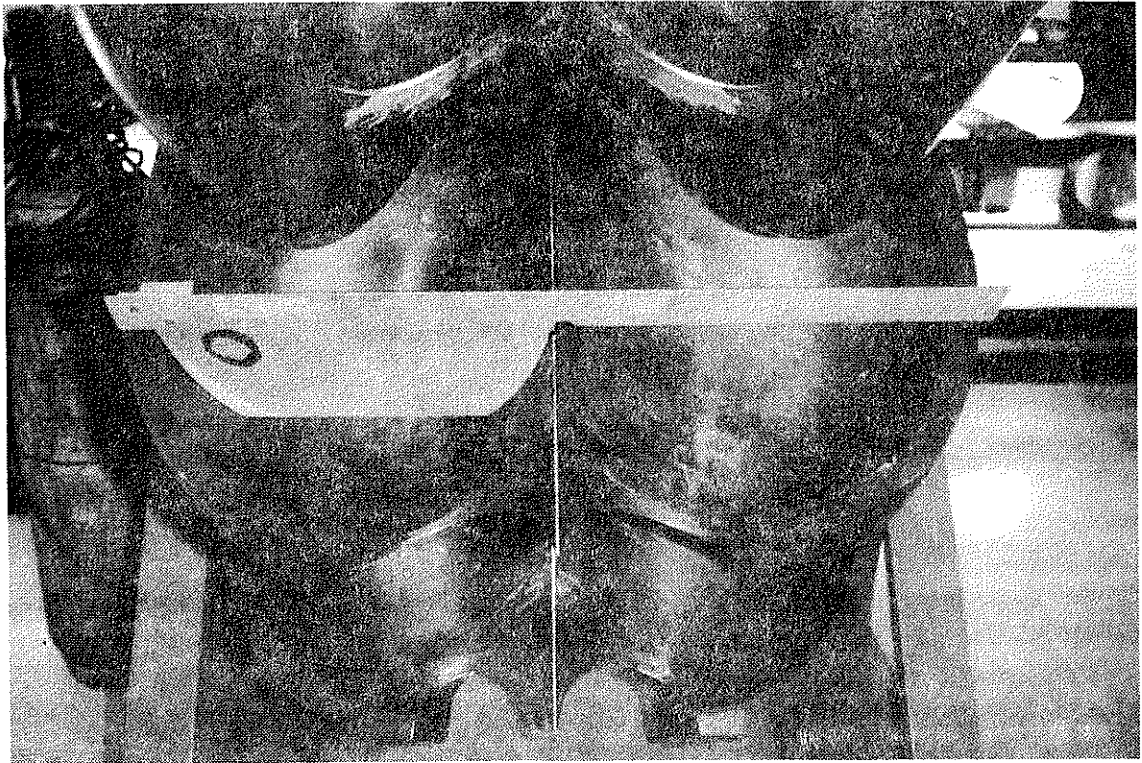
Medición interior, parte frontal, Plantilla No. 2.
